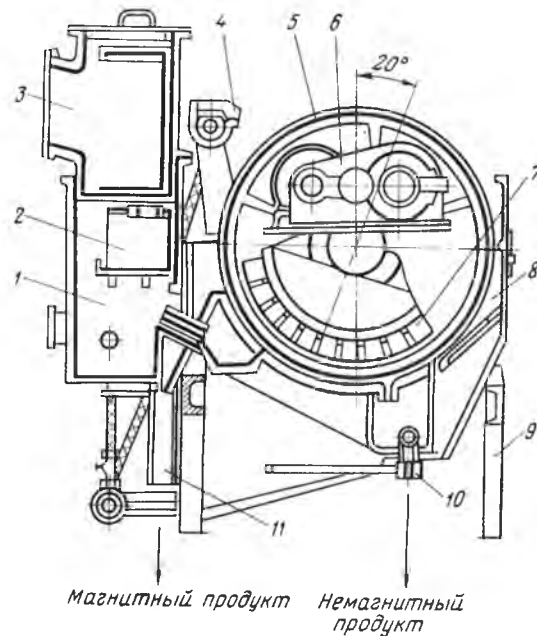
Барабанный магнитный сепаратор ПБМ-120/300:
